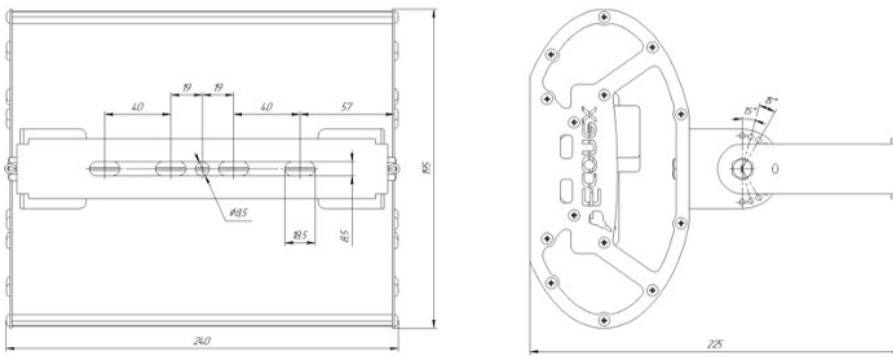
Габаритный и присоединительный чертеж светильника Econex Board 24
